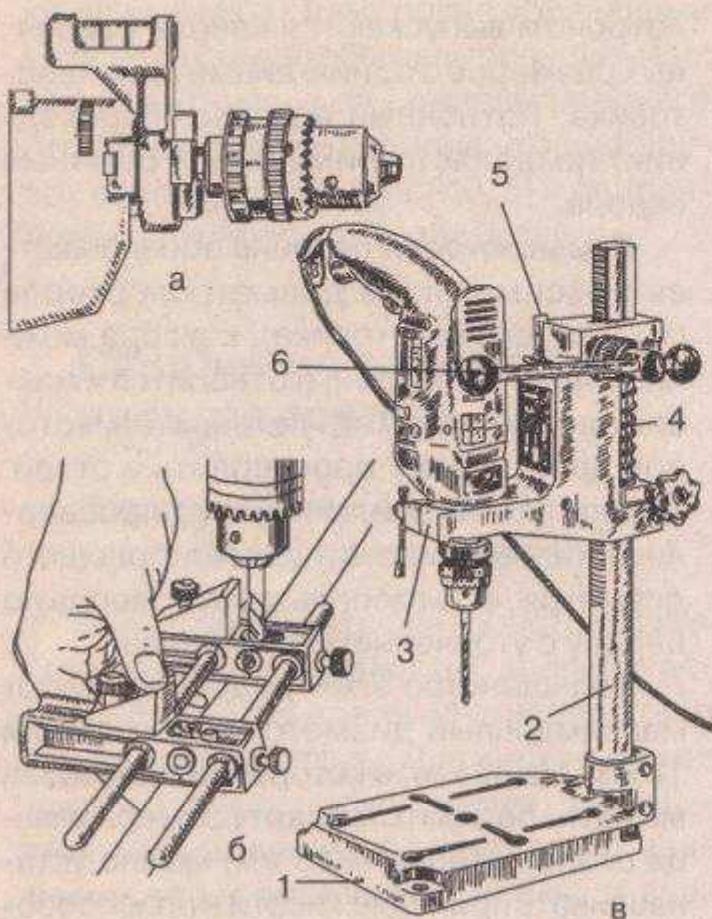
Приспособления для электродрели: а — спиртовой уровень для контроля положения дрели; б — нагельный кондуктор для сверления отверстий под нагели или штифты; в — вертикальная стойка; 1 — станина; 2 — вертикальная штанга; 3 — зажим; 4 — возвратная пружина; 5 — регулятор глубины; 6 — рычаг подачи
